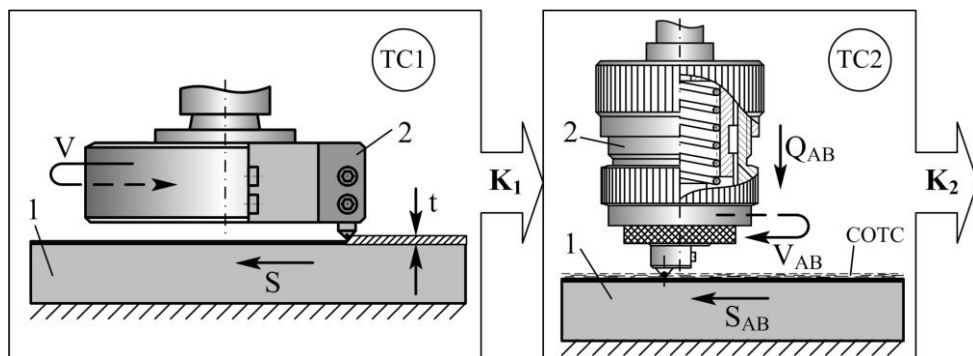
Технологическая система обработки плоских поверхностей деталей из чугуна торцевым фрезерованием (ТС1) и последующим алмазным выглаживанием (или накатыванием шариком) (ТС2) с применением инструментов, оснащённых ССТМ: 1 – обрабатываемая заготовка; 2 – инструмент
